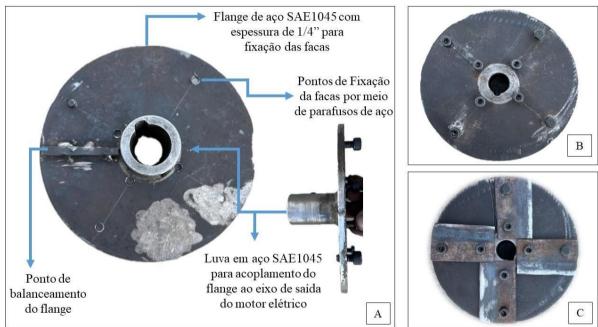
Flange fabricado em torno mecânico, em chapa de aço SAE1045 com espessura de 1/4". A) Vista inferior do flange, B) Vista superior do flange sem facas, C) Vista superior do flange com quatro facas fixadas por meio de parafusos. Fonte autoria própria.
